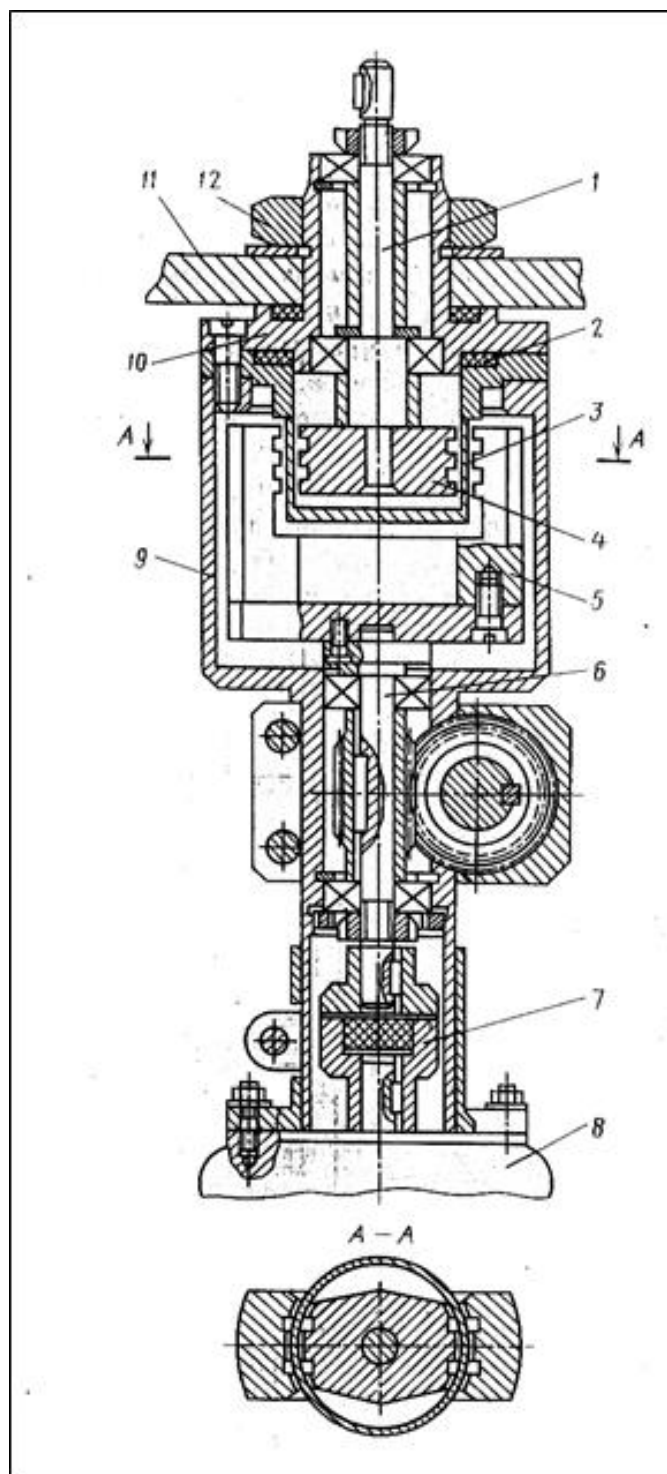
Вакуумный ввод вращательного движения с бесконтактным магнитным взаимодействием: 1 – ведомый вал; 2 – прокладка; 3 – стакан; 4 – ярмо; 5 – магнит; 6 – ведущий вал; 7 – упругая муфта; 8 – электродвигатель; 9 – корпус; 10 – втулка; 11 – стенка вакуумной камеры; 12 – гайка
